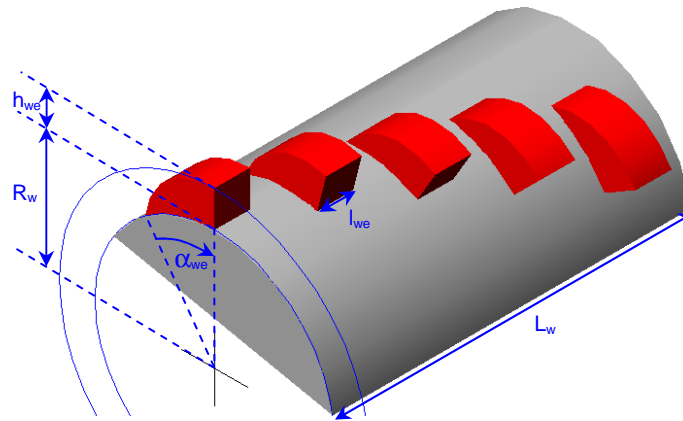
Werkzeug- und Grundkörperabmessungen zur Charakterisierung der Werkzeugmakroform.
